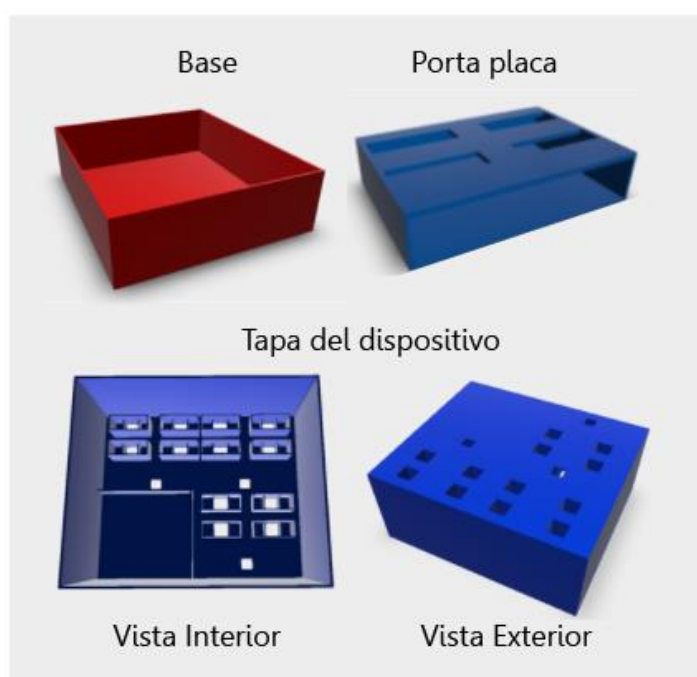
Estructura del dispositivo en 3D: base, porta placa, y tapa (vista interior y exterior).
